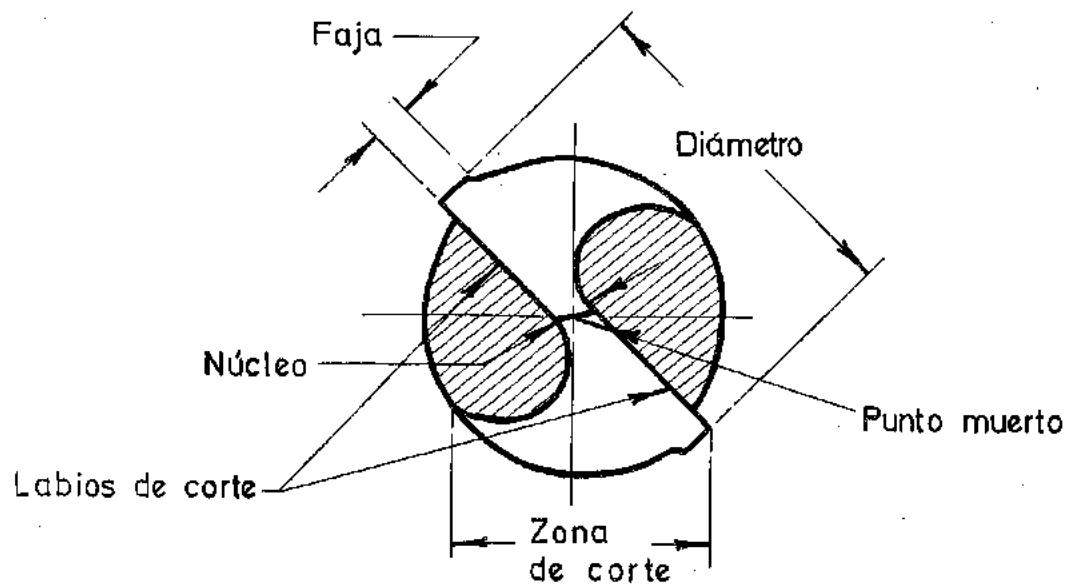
Punta de una broca helicoidal (Morse Twist Drill & Machine Co.)
